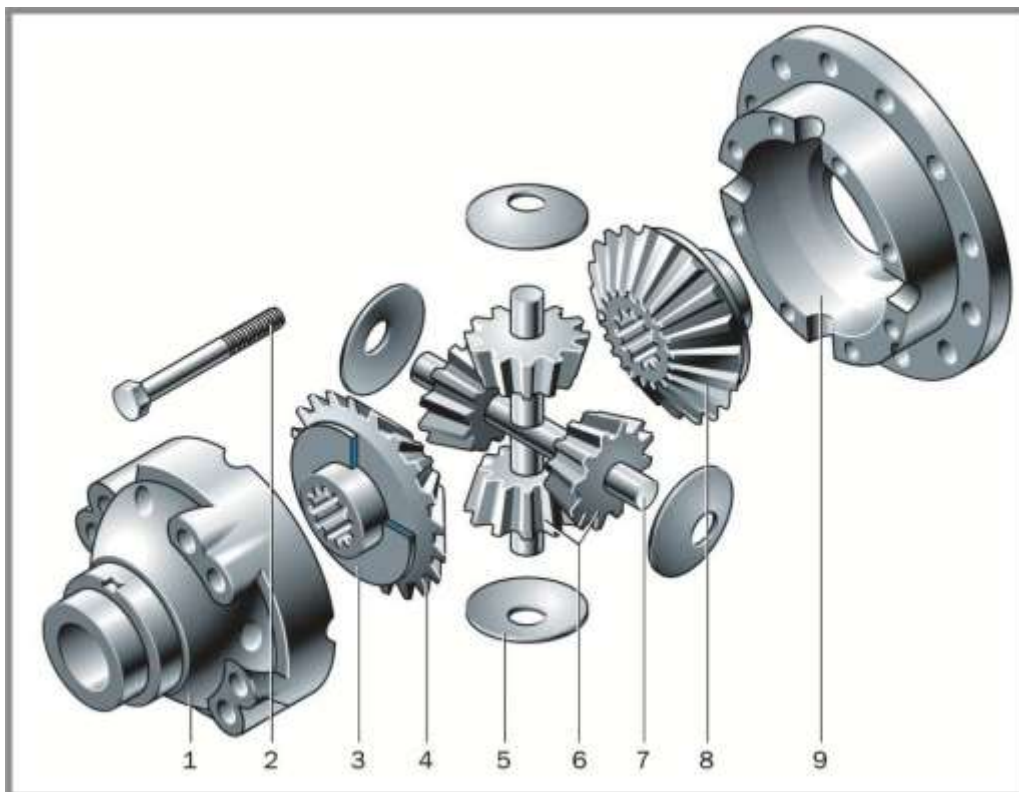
Деталі конічного симетричного диференціала: 1 – права коробка сателітів диференціала; 2 – болт коробки сателітів; 3 – опорна шайба шестерні; 4, 8 – напівосьові шестерні; 5 – опорна шайба сателіта; 6 – сателіти; 7 – вісь сателітів; 9 – ліва коробка сателітів диференціала
